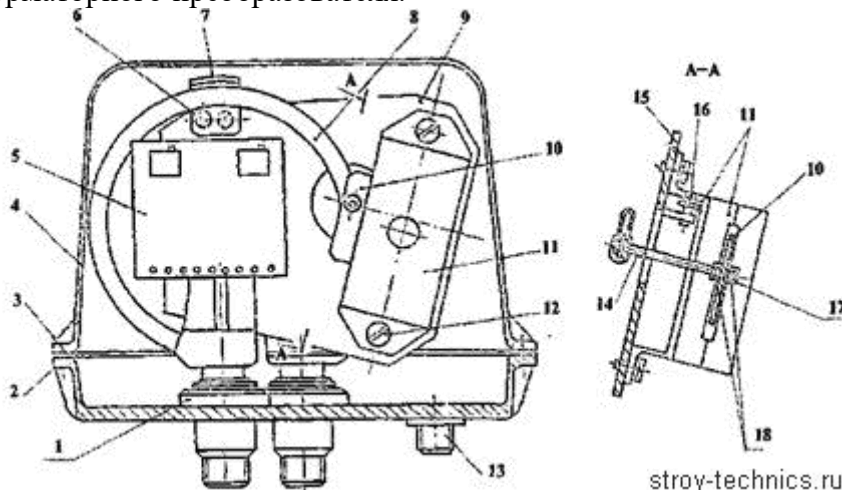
Датчик усилий манометрический: 1 — штуцерное соединение; 2 — основание; 3 — прокладка; 4 — крышка; 5 — плата; 6, 12 — винты; 7 — упор; 8 — манометрическая трубка; 9 — корпус; 10 — экран; 11 — блок катушек; 13 — разъем; 14 — стойка; 15 — плата; 16 — регулировочный винт; 17 — гайка; 18 — шайбы.
